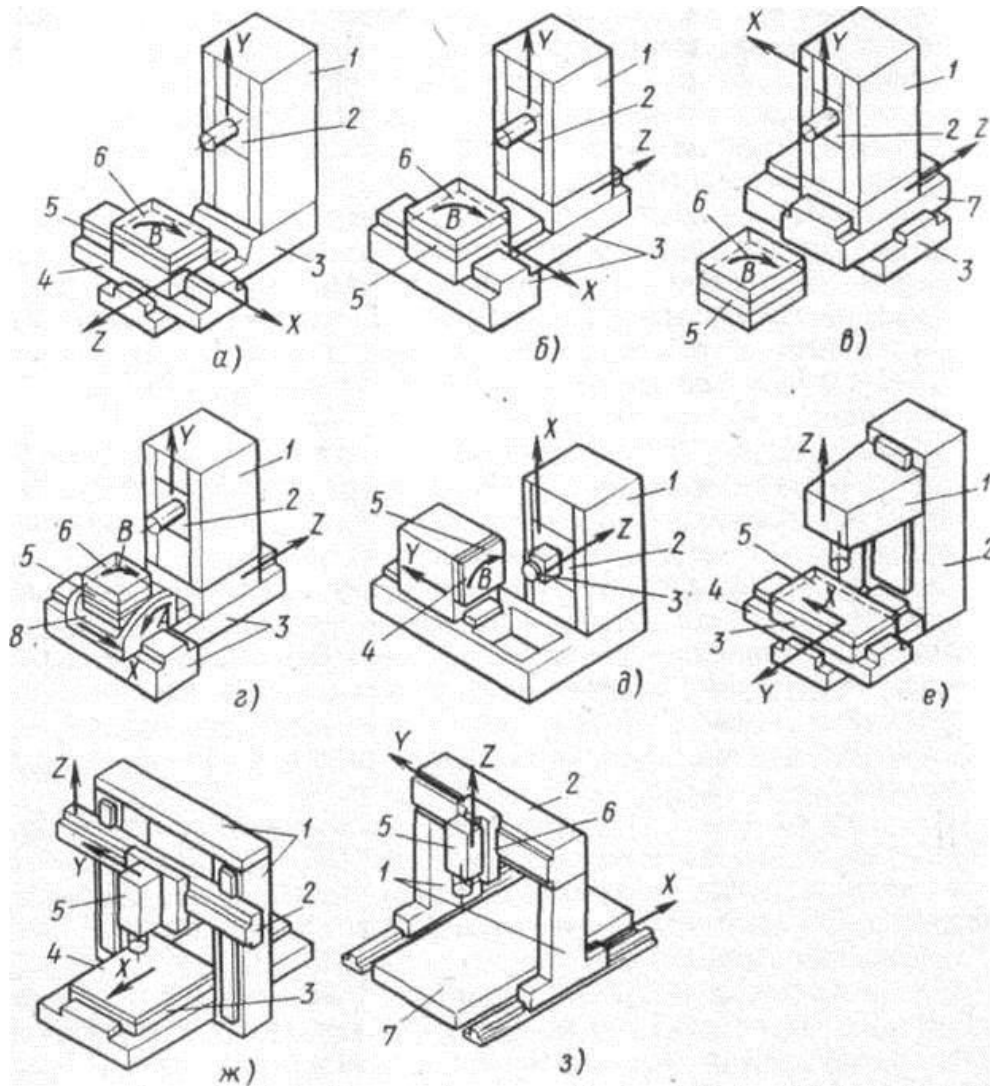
Компоновки багатоопераційних та фрезерних верстатів з ЧПК
